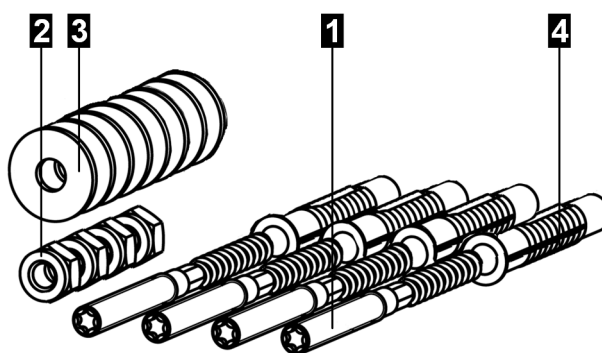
Kit di fissaggio per il montaggio a parete
